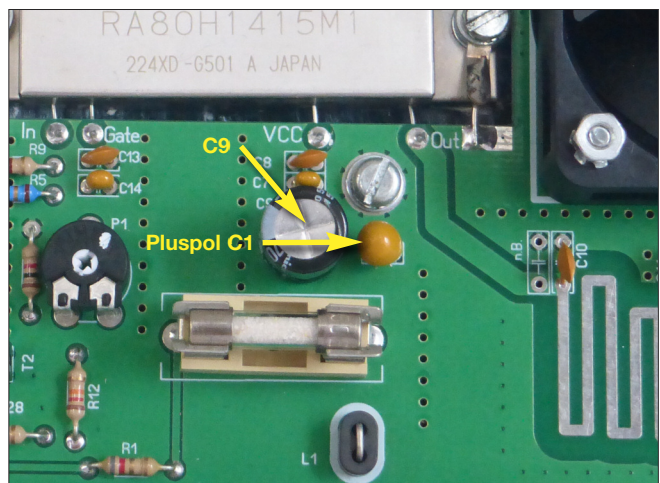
Leiterplattenausschnitt mit einigen Bauelementen der Kompletierung
